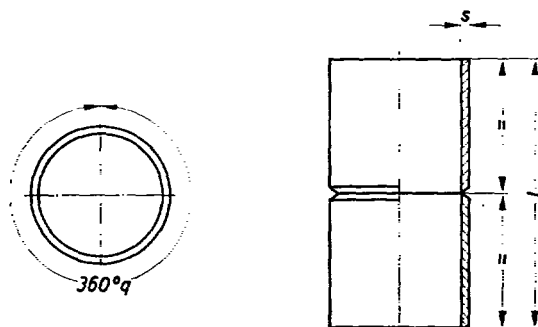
Stumpfnah-Prüfstück für Rohrschweißer in Schweißposition q (Maße siehe Tabelle 7)
